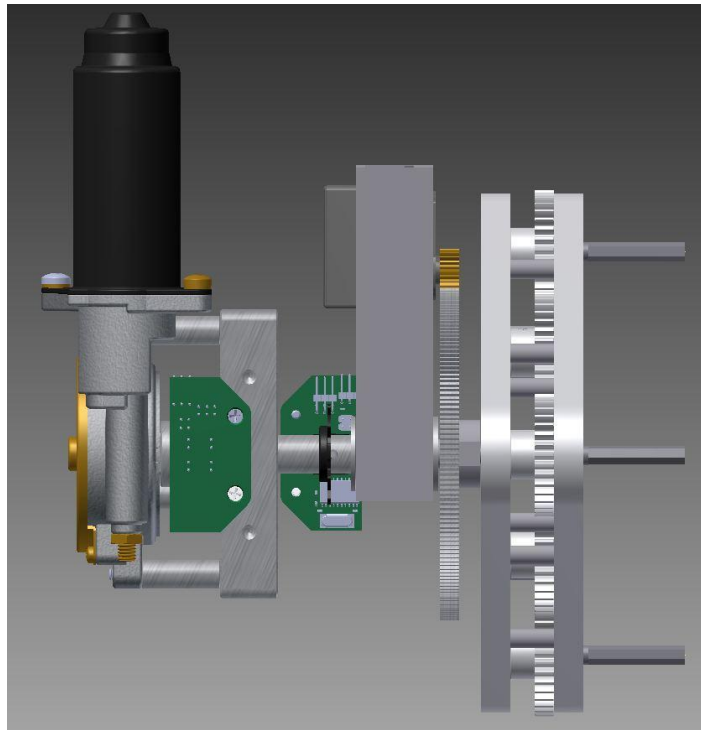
Acoplamiento del motor DC Parallax con el eje de transmisión del engranaje solar
